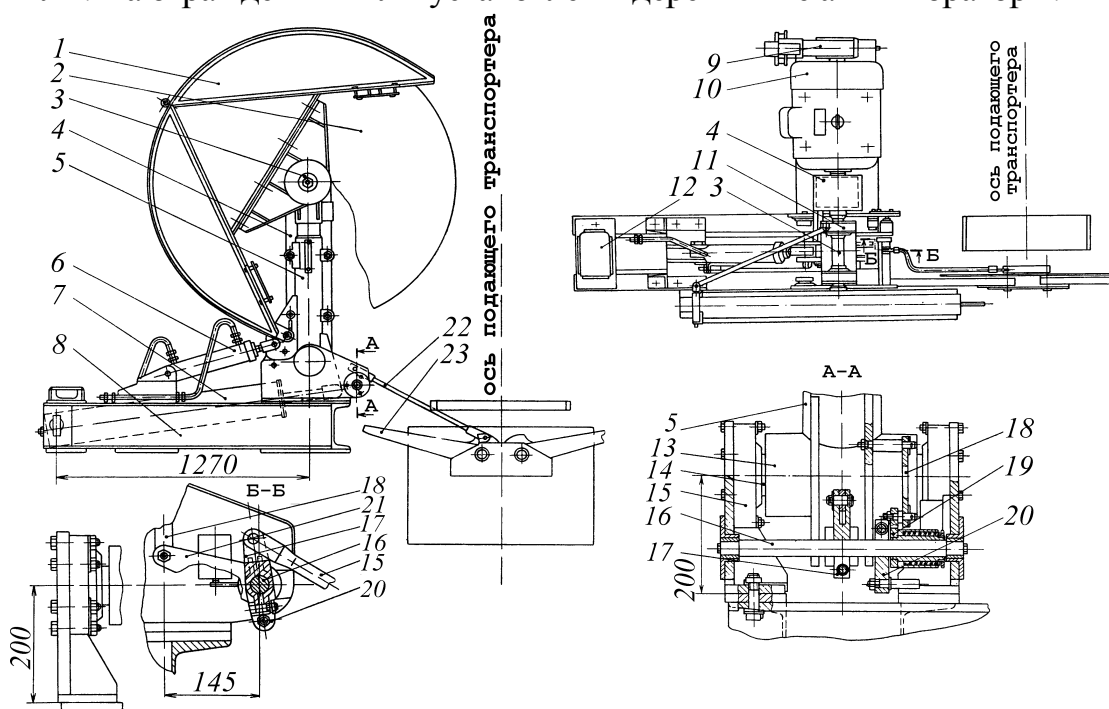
Автоматическая пила АЦ-ЗС: 1 – ограждение пилы; 2 – пильный диск; 3 – пильный вал; 4 – ограждение клиноременной передачи; 5 – маятник; 6 – гидроцилиндр подачи пилы; 7 – демпфер; 8 – рама; 9 – тормоз; 10 – электродвигатель; 11 – корпус подшипников пильного вала; 12 – электрооборудование; 13 – нижняя труба маятника; 14 – ось маятника; 15 – корпус подшипника; 16 – вал; 17 – рычаг поворота вала; 18 – тяга; 19 – рычаг переключения движения маятника; 20 – рычаг промежуточного останова; 21 – поводок рычага переключения; 22 – тяга; 23 – рычаг центрирующего устройства
